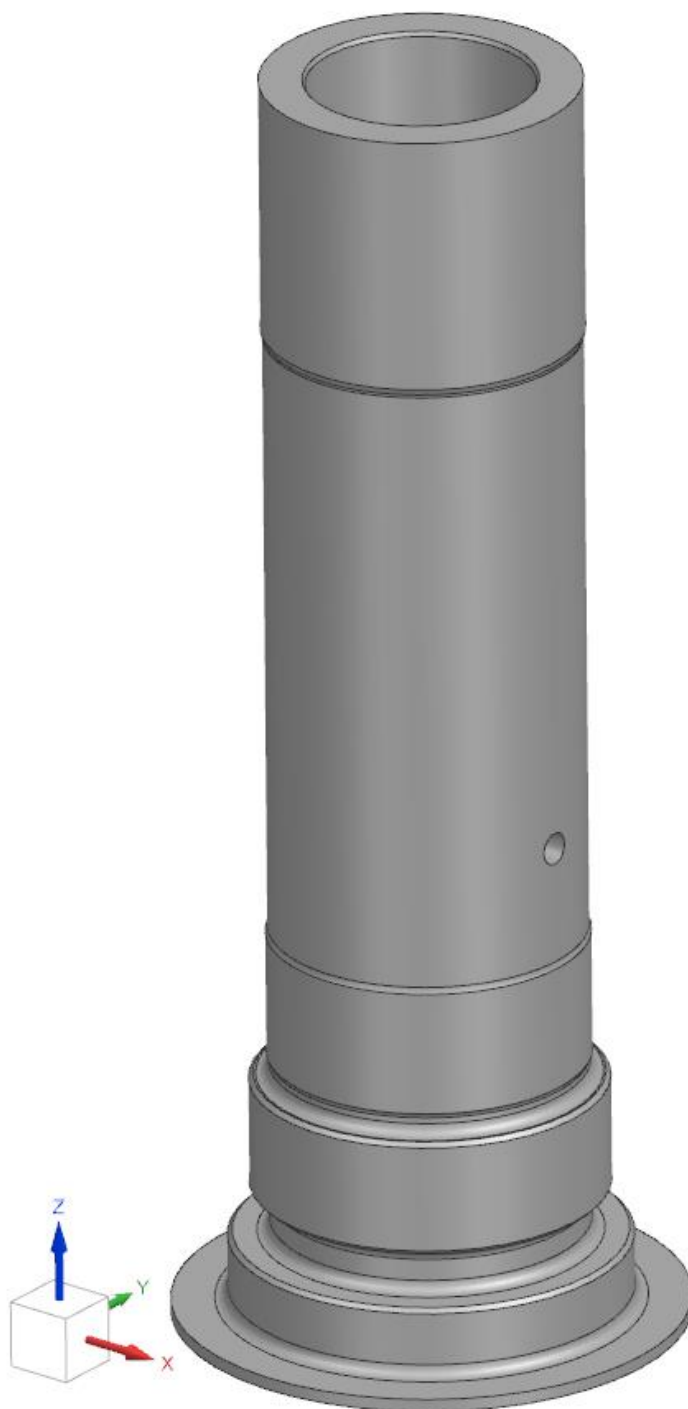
Створення 3д моделі деталі після обробки
